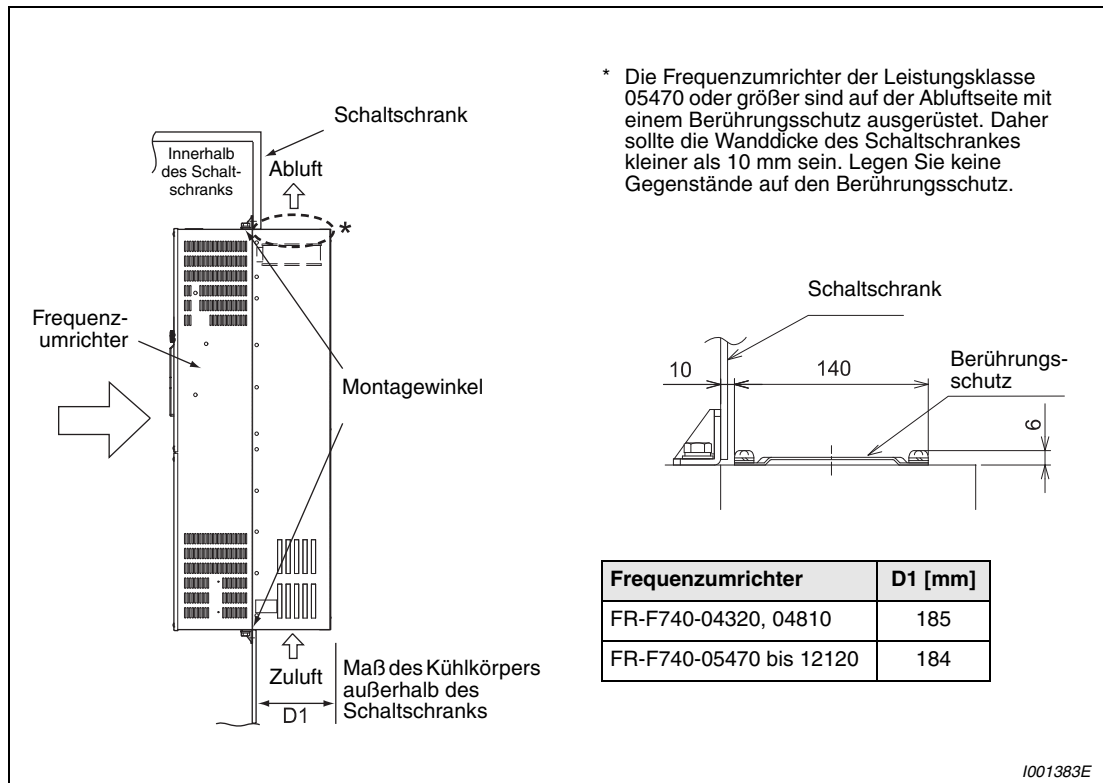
Montage des Frequenzumrichters zur externen Kühlluftführung
